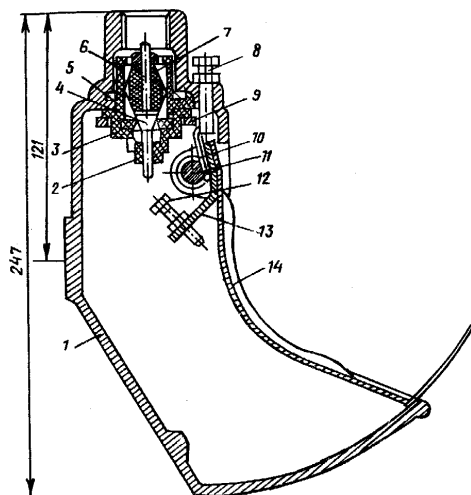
Автонапувалка індивідуальна клапанного типу ПСС-1:1-чаша; 2-кришка клапана; 3-сідло; 4-клапан; 5 –прокладка; 6-стакан; 7-амортизатор; 8-регульований болт важеля; 9-притискне кільце; 10-пружина; 11-вісь; 12-регулювальний болт ходу клапана; 13-натискний важіль; 14-кришка чаші.
